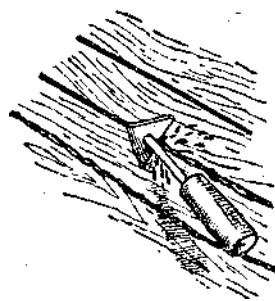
Затвердевшая заливка, выступающая над поверхностью палубы, удаляется с помощью шкрабки
